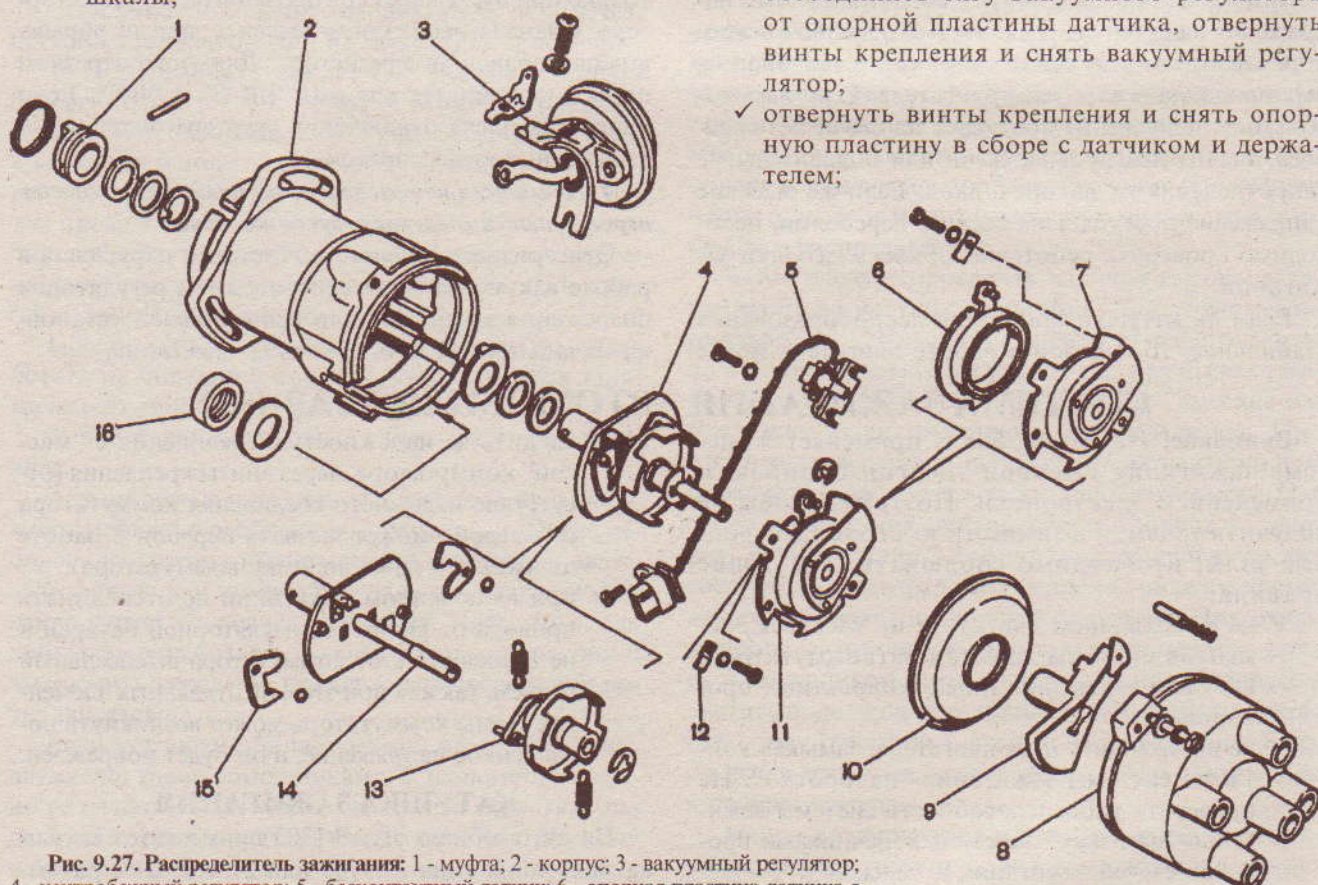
Распределитель зажигания: 1 - муфта; 2 - корпус; 3 - вакуумный регулятор; 4 - центробежный регулятор; 5 - бесконтактный датчик; 6 - опорная пластина датчика с подшипником; 7 - держатель переднего подшипника валика; 8 - крышка; 9 - ротор; 10 - защитный экран; 11 - держатель переднего подшипника валика в сборе с опорной пластиной датчика; 12 - шайба крепления проводов; 13 - ведомая пластина центробежного регулятора с экраном; 14 - валик с ведущей пластиной центробежного регулятора; 15 - грузики; 16 - сальник
